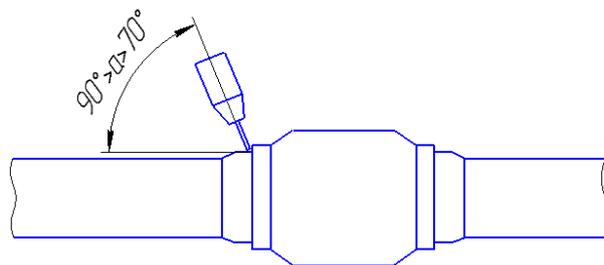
Сварка трубы средней и компенсатора
